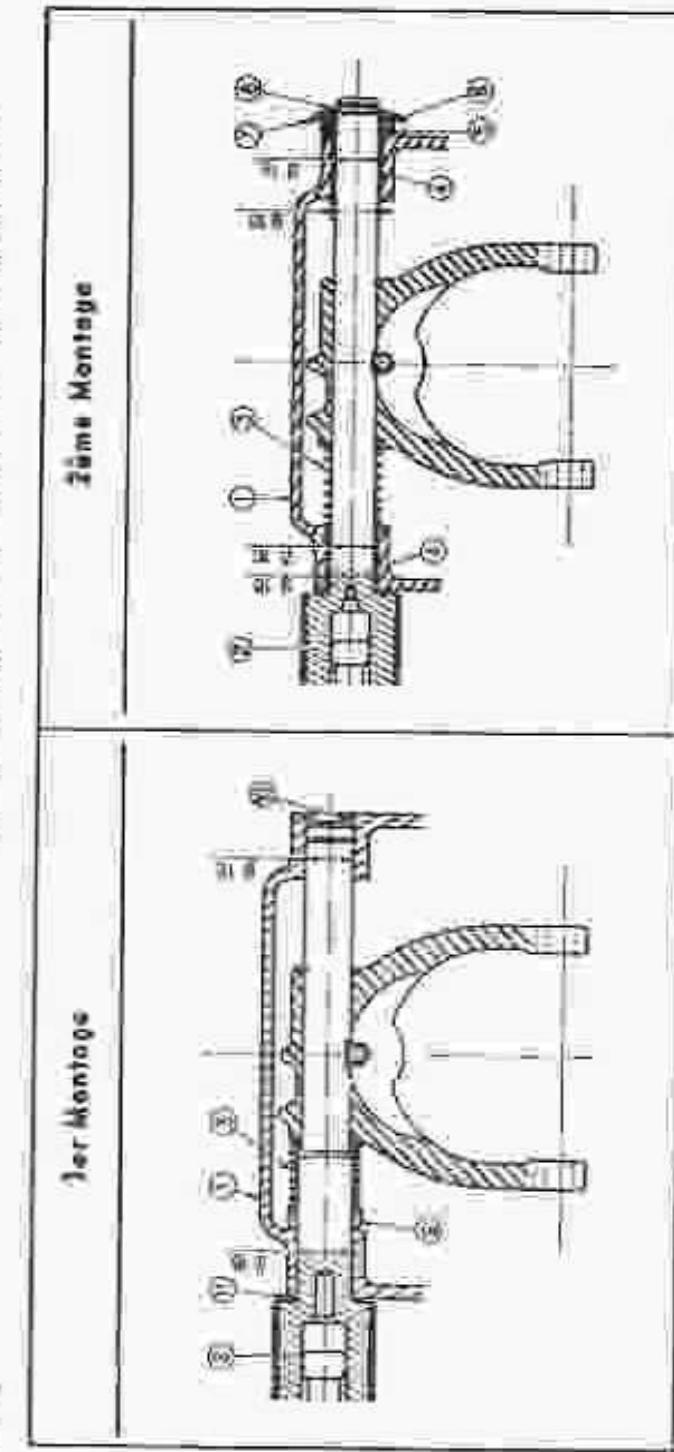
Vue en coupe de l'assemblage cylindre.
